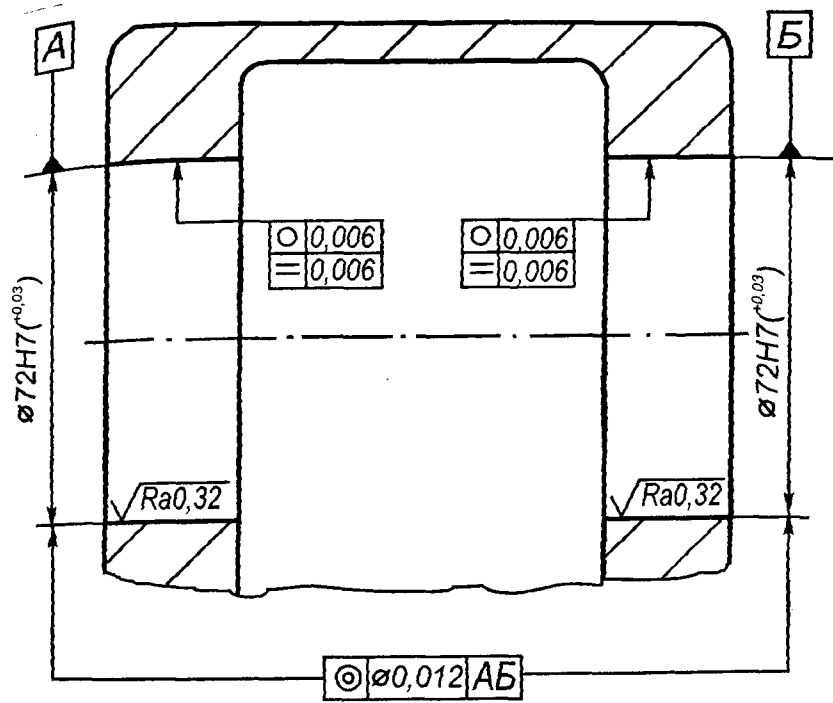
Пример обозначения точностных требований к поверхностям отверстий корпуса, сопрягаемым с подшипником качения
